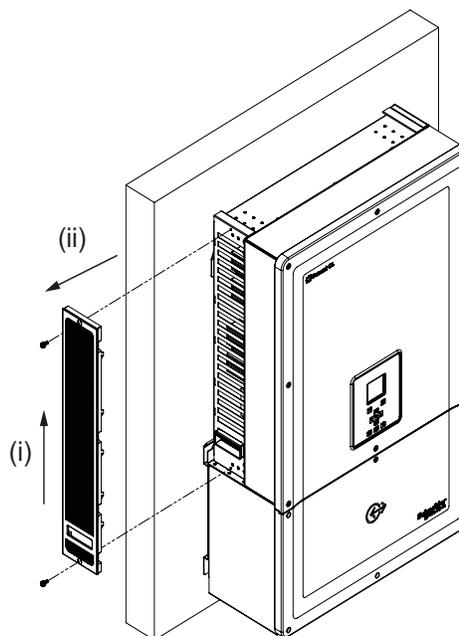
Remover a tampa da abertura de ventilação – lado esquerdo
